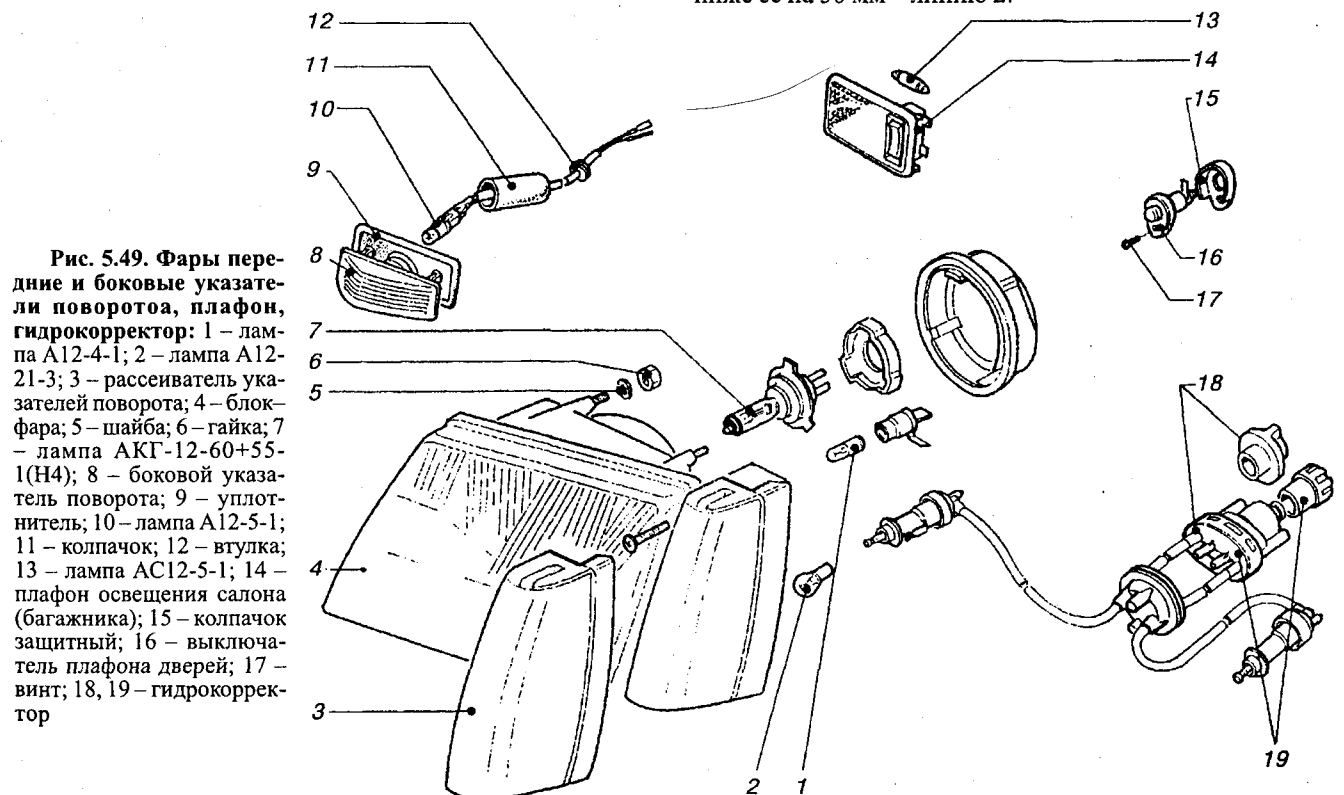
Фары передние и боковые указатели поворота, плафон, гидрокорректор: 1 – лампа А12-4-1; 2 – лампа А12-21-3; 3 – рассеиватель указателей поворота; 4 – блок-фара; 5 – шайба; 6 – гайка; 7 – лампа АКГ-12-60+55-1 (Н4); 8 – боковой указатель поворота; 9 – уплотнитель; 10 – лампа А12-5-1; 11 – колпачок; 12 – втулка; 13 – лампа АС12-5-1; 14 – плафон освещения салона (багажника); 15 – колпачок защитный; 16 – выключатель плафона дверей; 17 – винт; 18, 19 – гидрокорректор
